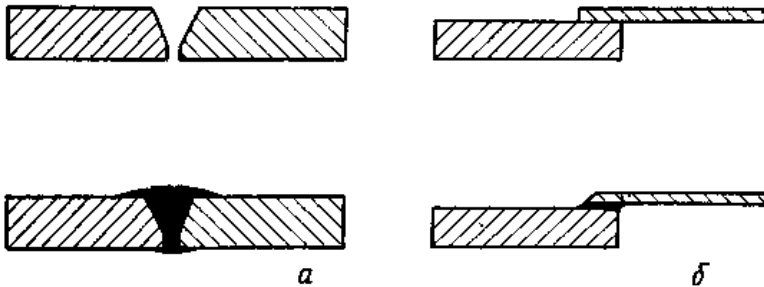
Схема образования шва при пайке-сварке:
